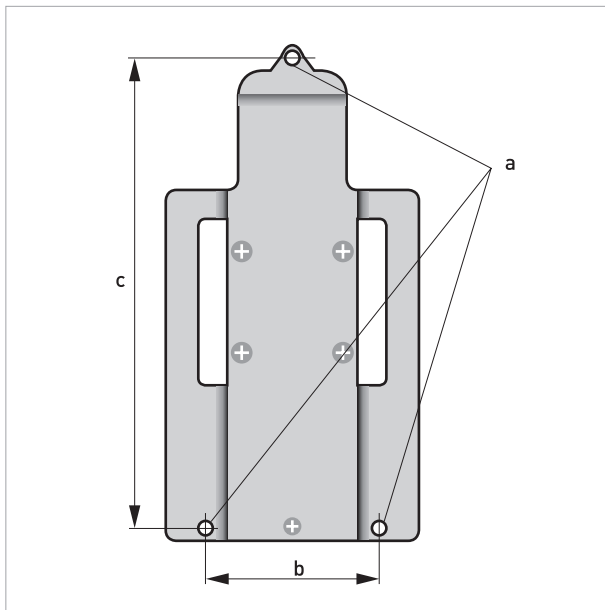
Размеры монтажной пластины корпуса для настенного монтажа из алюминия
